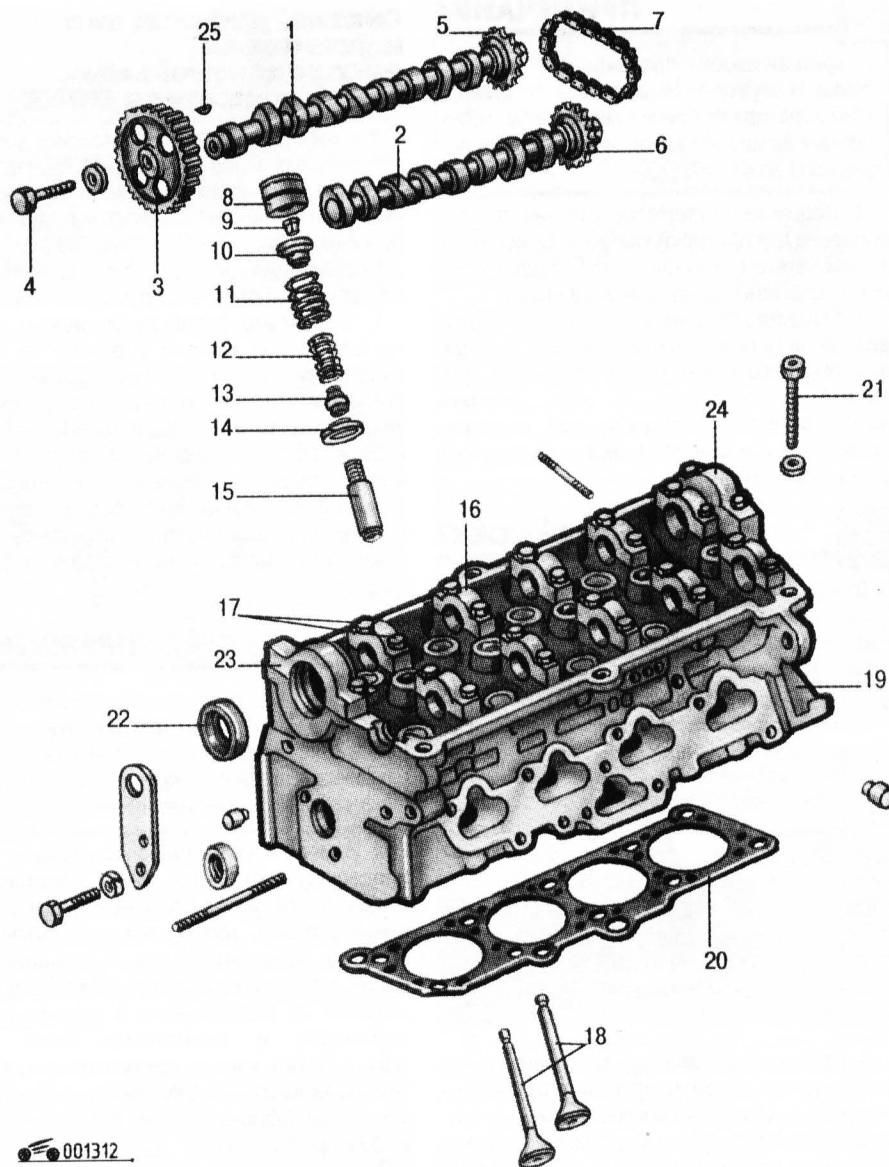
Головка блока цилиндров двигателя DOHC и механизм привода клапанов: 1 – распределительный вал выпускных клапанов; 2 – распределительный вал впускных клапанов; 3 – зубчатый шкив привода распределительного вала выпускных клапанов; 4 – болт крепления зубчатого шкива; 5 – звездочка распределительного вала выпускных клапанов; 6 – звездочка распределительного вала впускных клапанов; 7 – цепь привода распределительного вала выпускных клапанов; 8 – гидрокомпенсатор; 9 – сухари клапана; 10 – верхняя тарелка пружин; 11 – наружная пружина клапана; 12 – внутренняя пружина клапана; 13 – маслосъемный колпачок; 14 – нижняя тарелка пружин; 15 – направляющая втулка клапана; 16 – крышка подшипника распределительного вала; 17 – болты крепления крышки подшипника распределительного вала; 18 – клапаны; 19 – головка блока цилиндров; 20 – прокладка головки блока цилиндров; 21 – болт; 22 – сальник распределительного вала выпускных клапанов; 23 – крышка переднего подшипника распределительного вала выпускных клапанов; 24 – крышка заднего подшипника распределительного вала выпускных клапанов; 25 – сегментная шпонка
